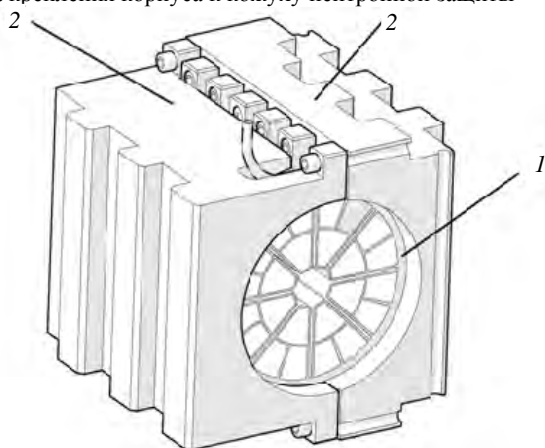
Внешний вид блока коллиматора в кожухе нейтронной защиты: 1 — блок нейтронного коллиматора; 2 — элементы кожуха нейтронной защиты портовой заглушки
